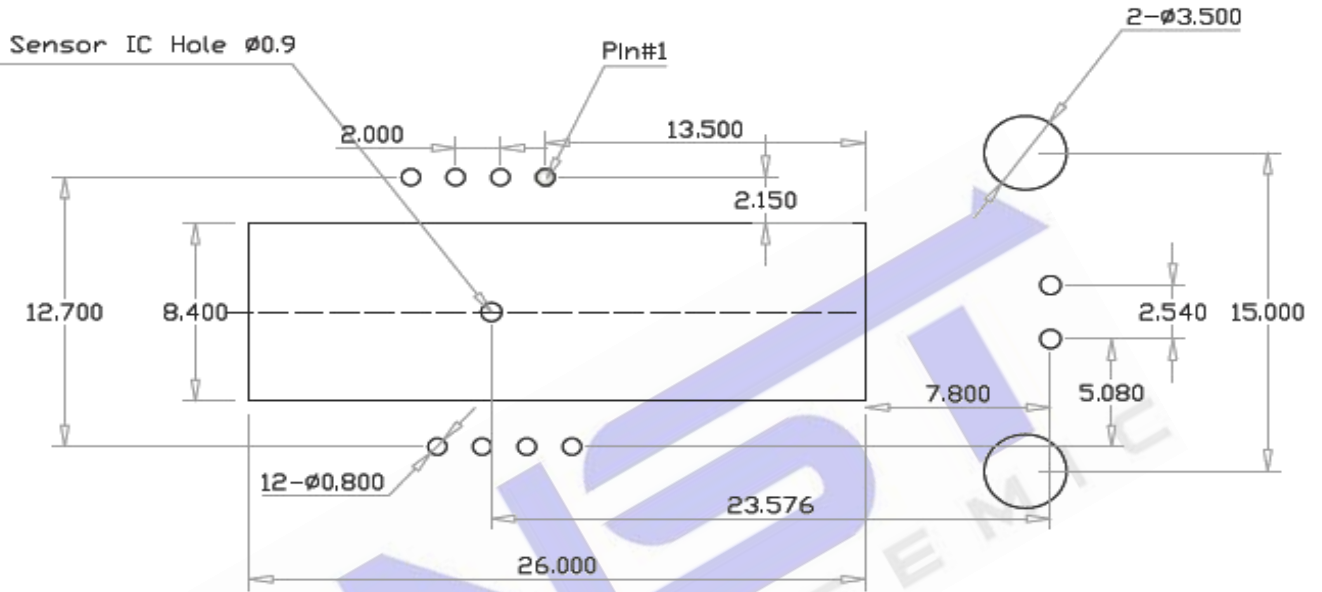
推荐 PCB 机械尺寸 (mm/inch)
